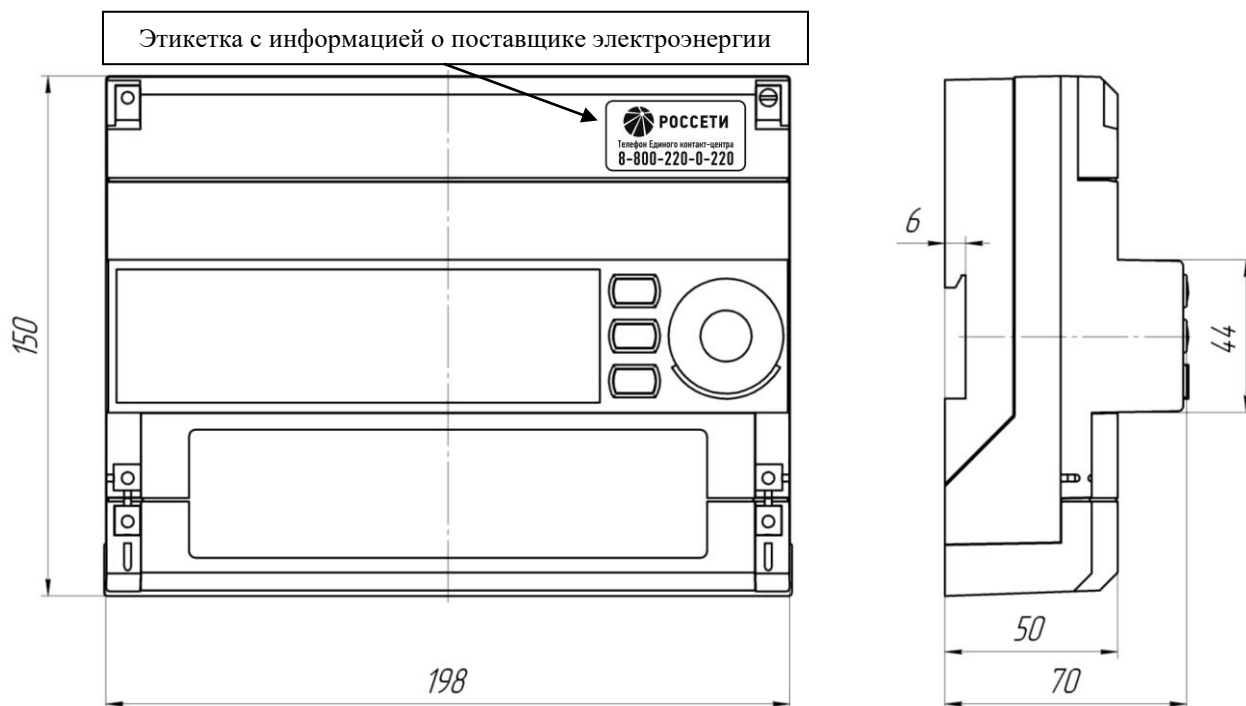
Габаритный чертеж и установочные размеры счётчика для установки на Din-рейку
